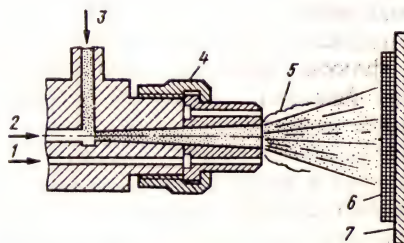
Схема газопламенного напыления: 1 — кислород и горючий газ; 2 — транспортирующий газ; 3 — напыляемый порошок; 4 — сопло; 5 — факел газового пламени; 6 — напыленная поверхность; 7 — напыляемая поверхность
